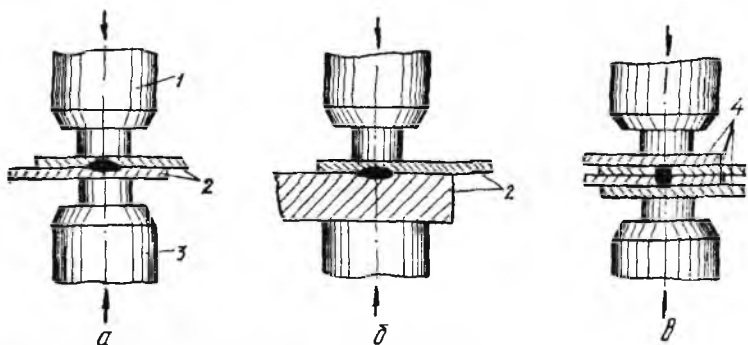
Схемы двусторонней точечной конденсаторной сварки.
